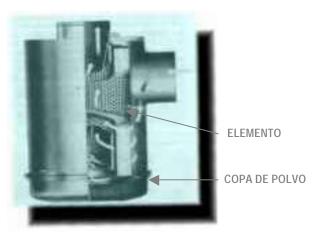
LA ESTRUCTURA DEL ELEMENTO FILTRANTE
